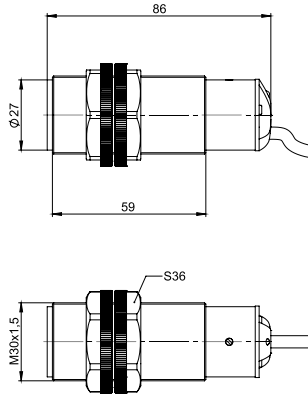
Габаритные и установочные размеры датчиков серии CAP30 с кабельным выводом
